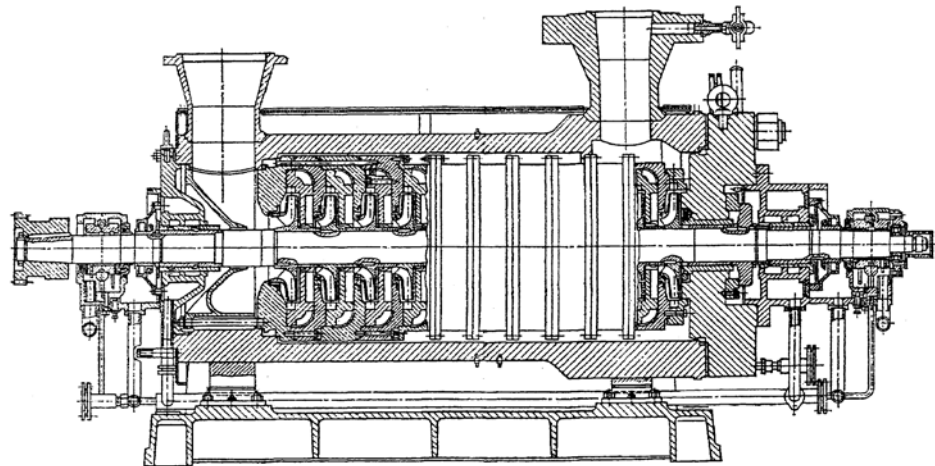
Живильний двохкорпусний відцентровий насос
